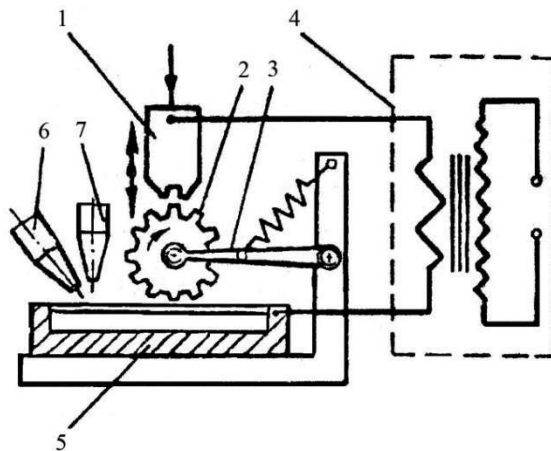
Схема припікання порошку на вершини зубів шестерні гідронасоса: 1 – верхній рухомий електрод; 2 – деталь; 3 – пристрій для підтримки деталі; 4 – джерело струму; 5 – нижній електрод з порошком; 6 – ємність для рідини; 7 – бункер для порошку
